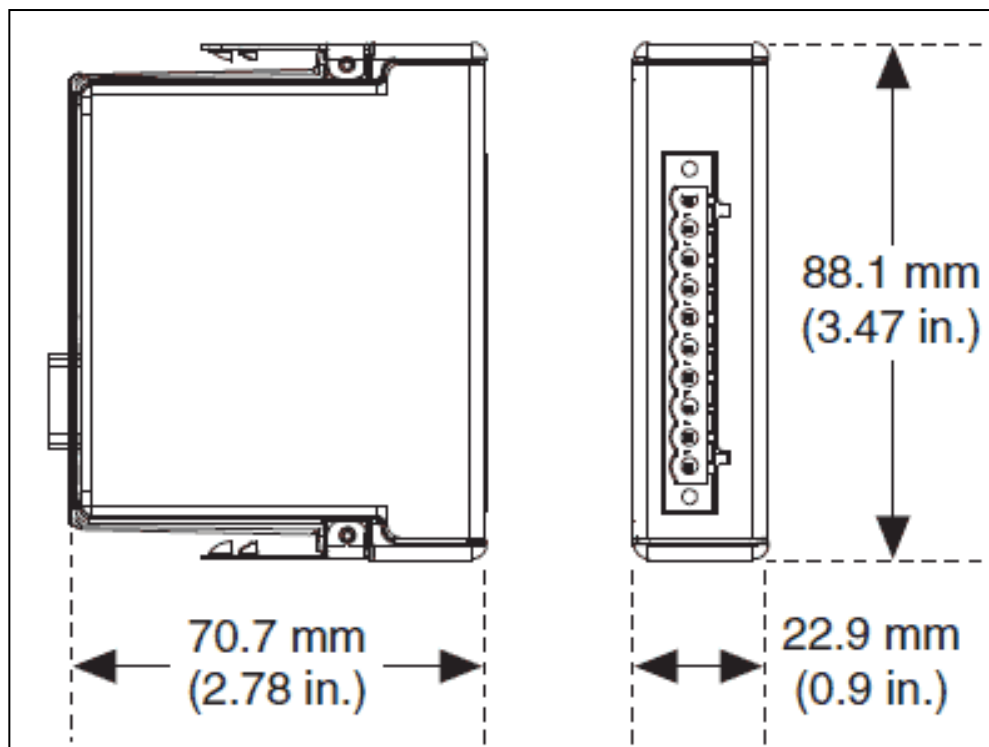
Módulo de E/S de la Serie C, Vista Frontal y Lateral con dimensiones.
